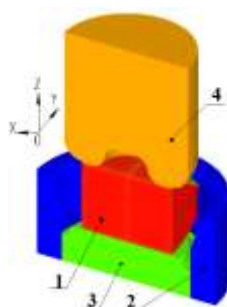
Схема зворотного видавлювання: 1 – заготовка, 2 – матриця, 3 – плита, 4 – пуансон
